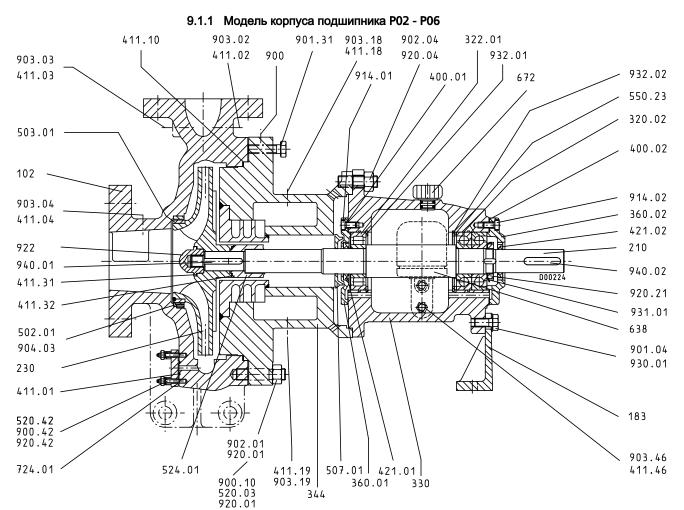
Обзорный чертеж корпуса подшипника модели Р02 - Р06
